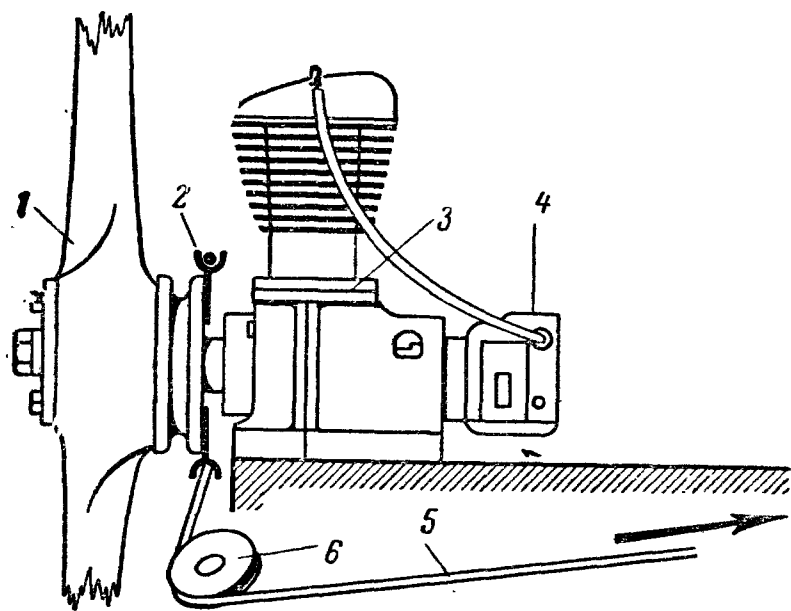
Принципиальная схема пускового устройства на аэросанях конструкции Л. Мисаева: 1 — воздушный винт; 2 — шкив на маховике двигателя; 3 — двигатель «ПД-10» с цилиндром «ИЖ-49»; 4 — магнет; 5 — пусковой ремень; 6 — ролик.
